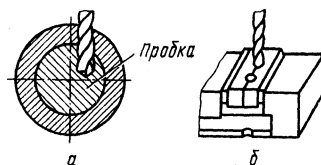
Приемы сверления: а — полый детали; б — полуотверстия
